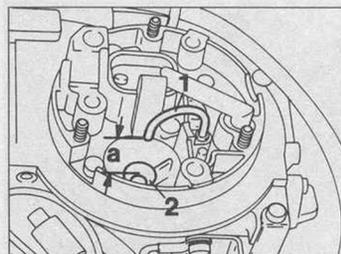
Регулировка трубы обогащения (Глава 16)
